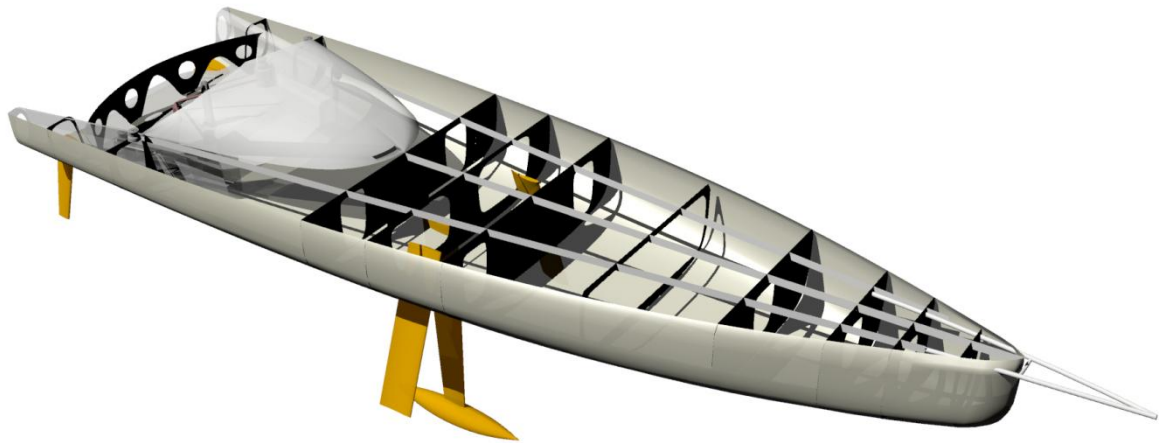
Disposición preliminar de los refuerzos de cubierta
